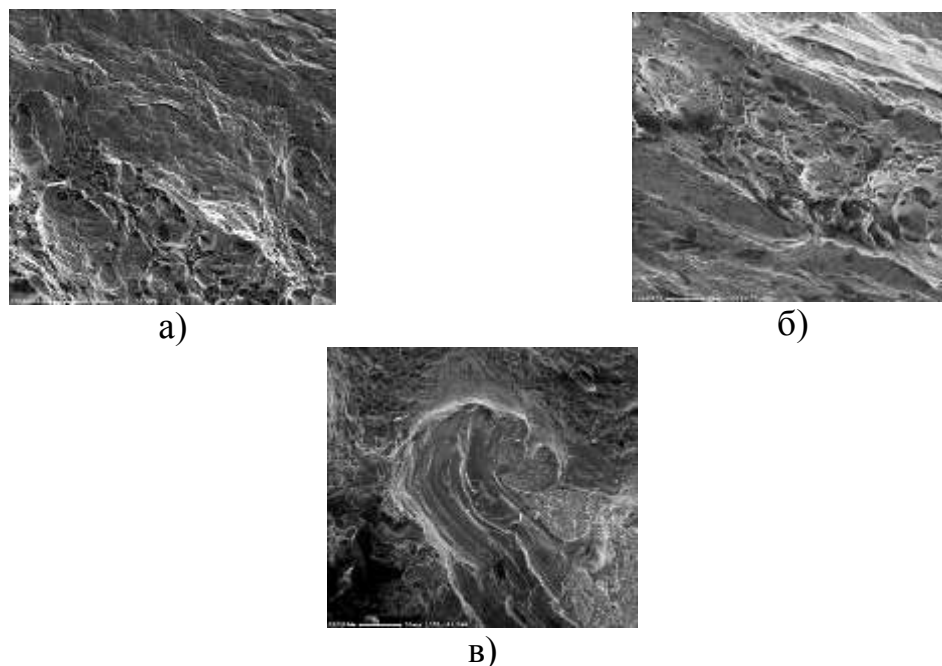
Вид поверхности разрушения образцов плакированной стали, изготовленных по различным технологическим схемам: а) электрошлаковая наплавка; б) пакетная прокатка; в) сварка взрывом.
